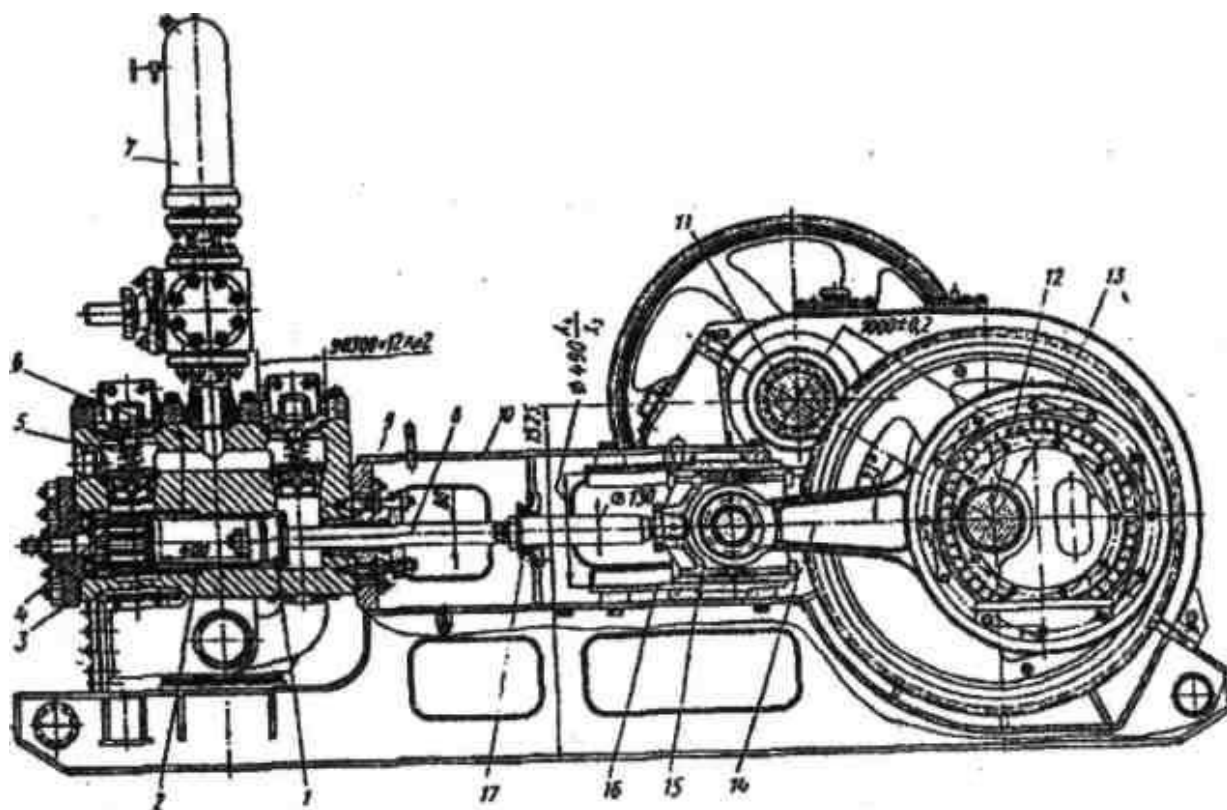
Приводной двухцилиндровый поршневой насос двойного действия
